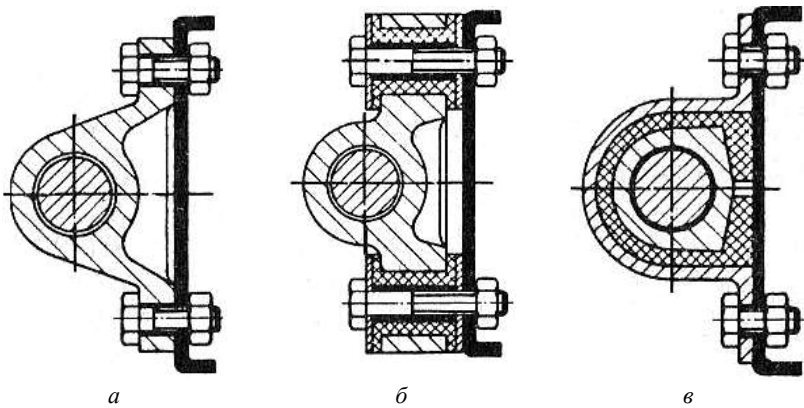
Варіанти кріплення корпусу рульового механізму:
